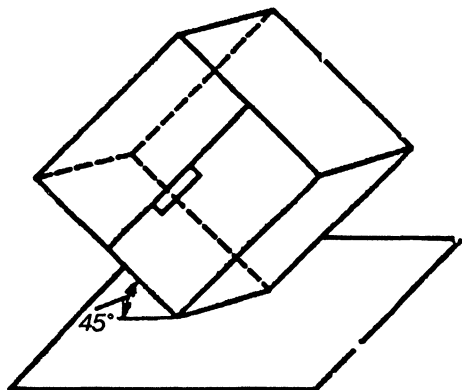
Схема проверки жесткости конструкции среднетоннажного контейнера установкой на продольное ребро
